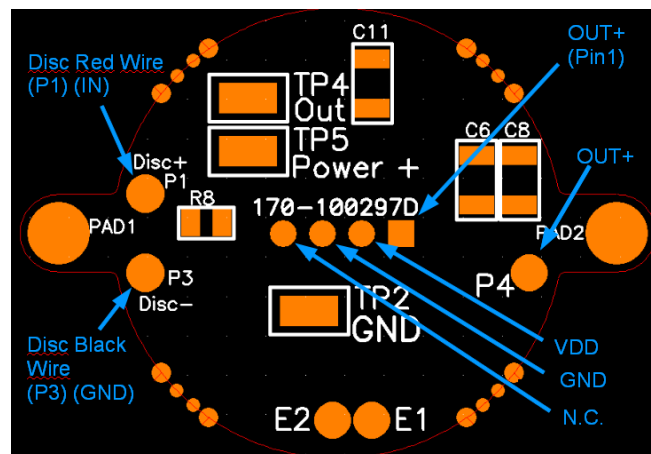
Vue du côté IC du PCB OEM Standard
